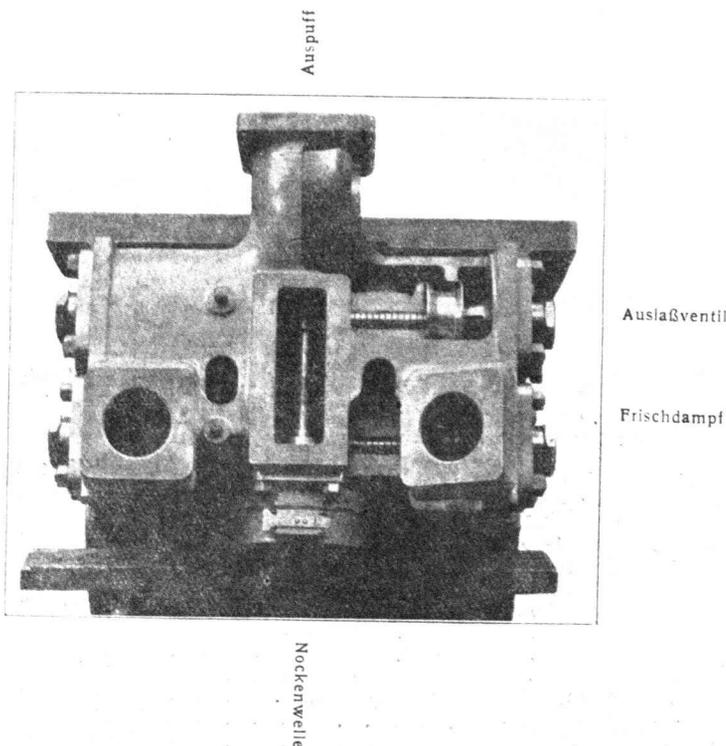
Draufsicht auf einen Dampfzylinder Reihe 80 mit aufgesetztem Ventilkasten.
